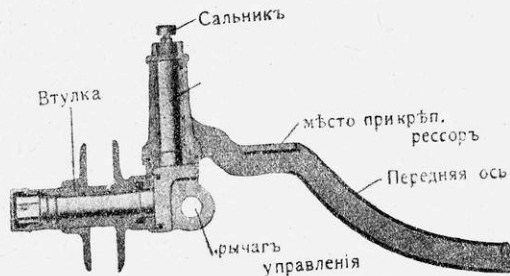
Ось со втулкой безъ шарикового подшипника.
